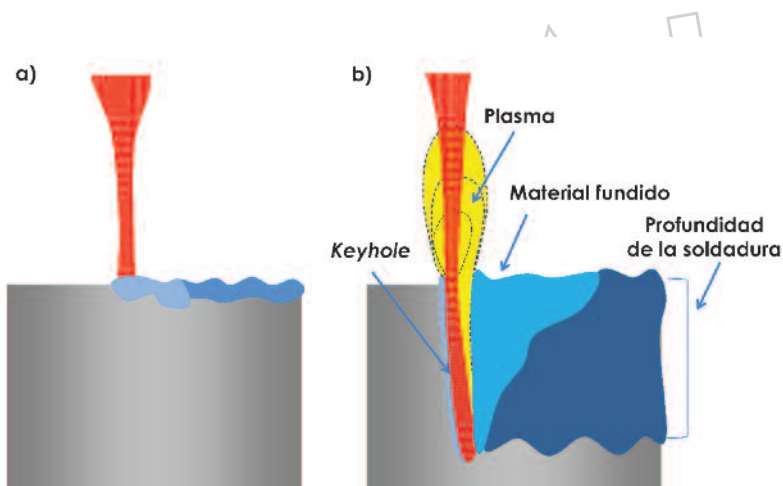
Tipos de soldadura láser. a) Limitada por conducción. b) Soldadura de penetración.
